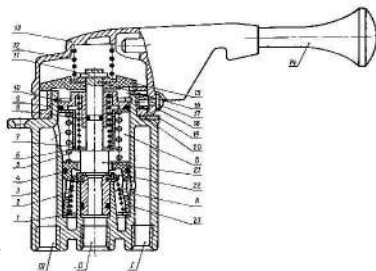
Тормозной кран обратного действия с ручным управлением: 1—упорное кольцо; 2—пружина клапана; 3—корпус; 4—уплотнительное кольцо; 5—уравновешивающая пружина; 6—пружина штока; 7—тарелка пружины; 8—направляющая штока; 9—обойма; 10—упорное кольцо; 11—штифт; 12—пружина; 13—крышка; 14—рукоятка; 15—направляющий колпачок; 16—шток; 17—ось ролика; 18—фиксатор; 19—ролик; 20—стопор; 21—выпускное седло клапана на штоке; 22—клапан; 23—следящий поршень; I—вывод к воздушному баллону; II—атмосферный вывод; III—вывод управляющей магистрали
